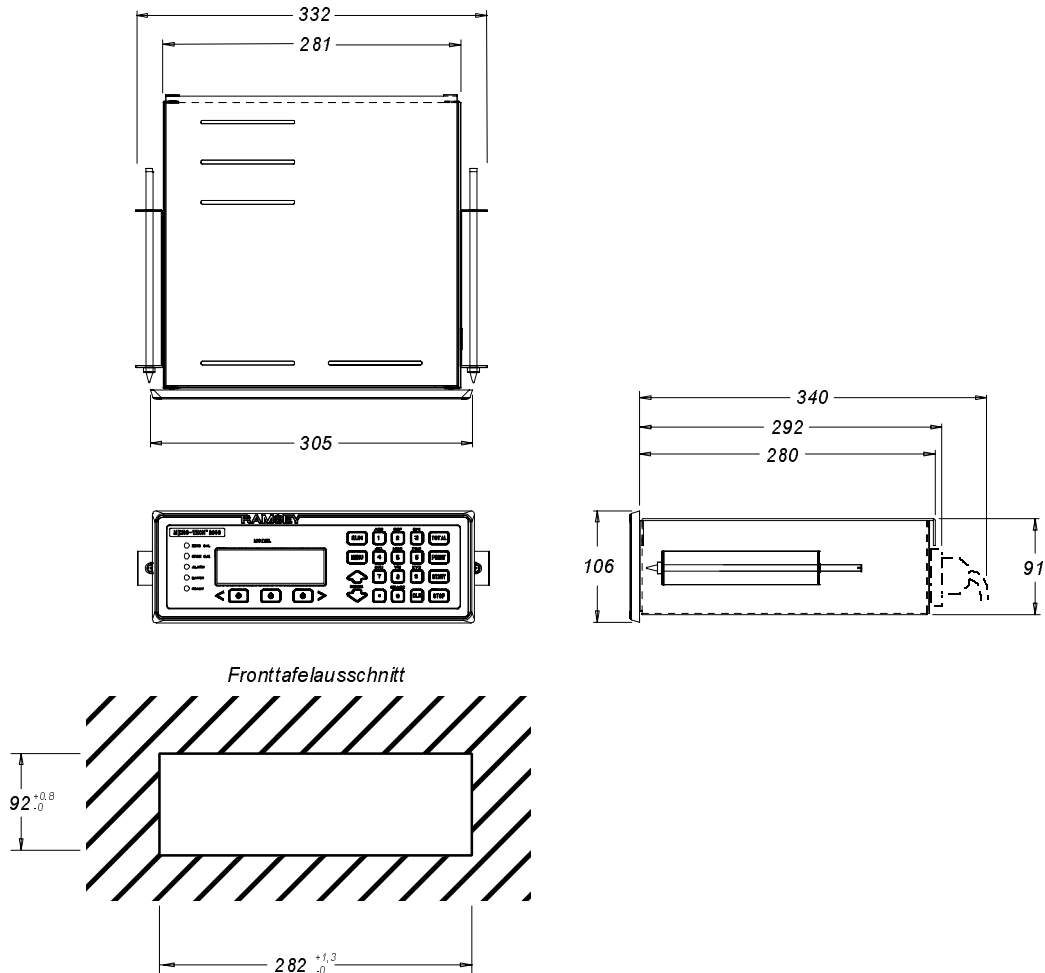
Einbaugehäuse Micro-Tech™ 2000 PM
